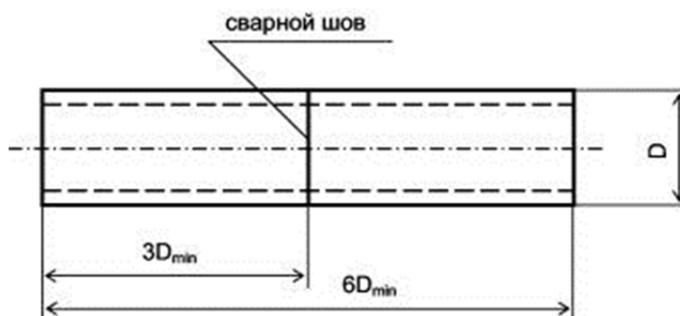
Эскиз трубчатого образца (тип XVIII по ГОСТ 6996-66) для испытаний на растяжение сварных соединений труб диаметром 20 мм
